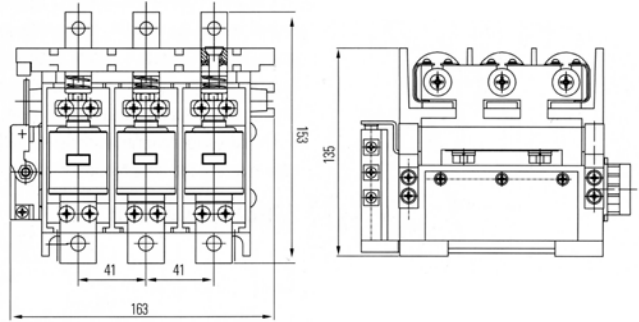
Габаритные размеры КВТ-1,14-80/125/160
